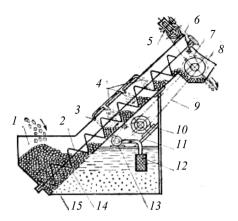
Схема работы измельчителя корнеклубнеплодов ИКС-5М: 1 — загрузочный бункер; 2 — шнековый транспортёр; 3 — напорная труба; 4 — патрубки с распределителями; 5 — редуктор; 6 — цепная передача; 7, 9 и 11 — клиноремённые передачи; 8 — измельчающий аппарат; 10 — электродвигатель; 12 — фильтр; 13 — центробежный насос; 14 — сетка; 15 — ванна для воды
